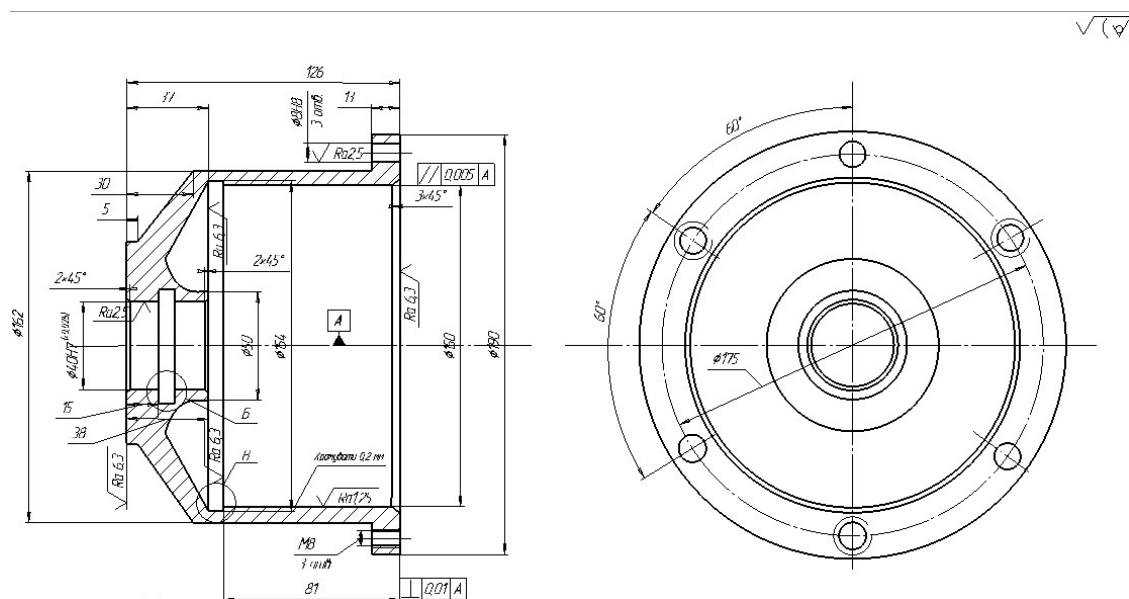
Креслення деталі корпуса одностороннього гідроциліндра
